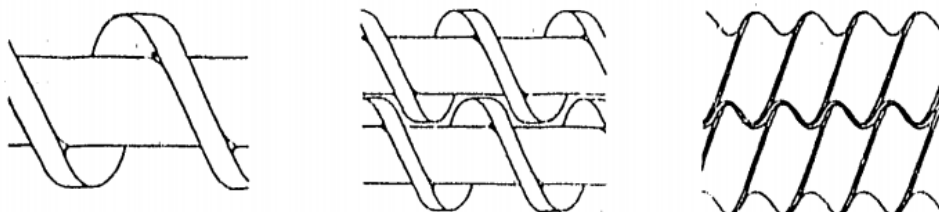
Schneckentypen: Einzelschnecke geschweißt, Doppelschnecke geschweißt, Doppelschnecke gedreht (Camp 1990)
